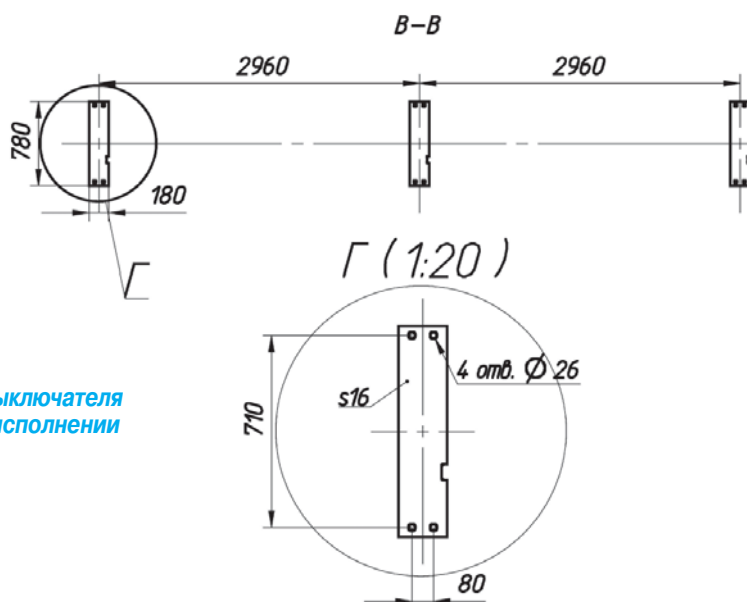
Установочные размеры рамы выключателя элегазового колонкового ВГТ-1А1-220 в исполнении без опорных конструкций.
